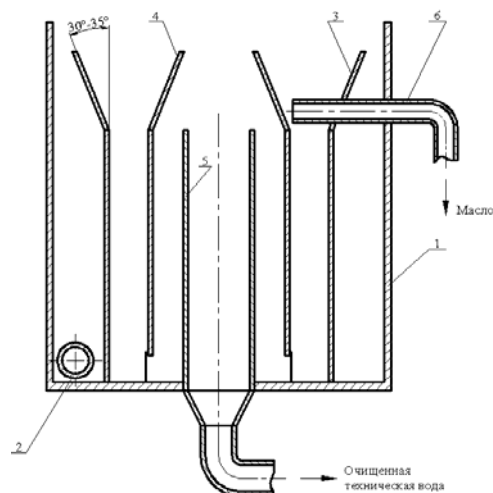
Маслоотделитель непрерывного действия: 1 – корпус; 2 – тангенциально врезанный патрубок; 3 – переливной цилиндр; 4 – накопитель очищенной технической воды; 5 – сливной патрубок; 6 – патрубок для отвода масла
